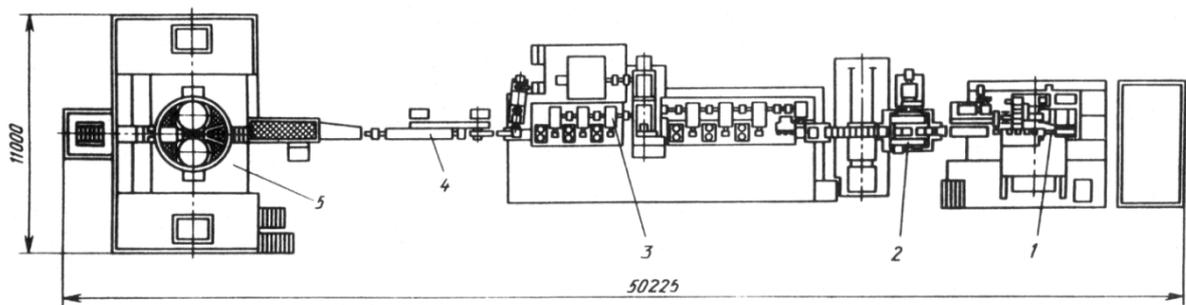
Схема литейно-прокатного агрегата: 1 – литейная машина; 2 – линия транспортировки заготовки; 3 – прокатный стан; 4 – участок охлаждения катанки; 5 – моталка
